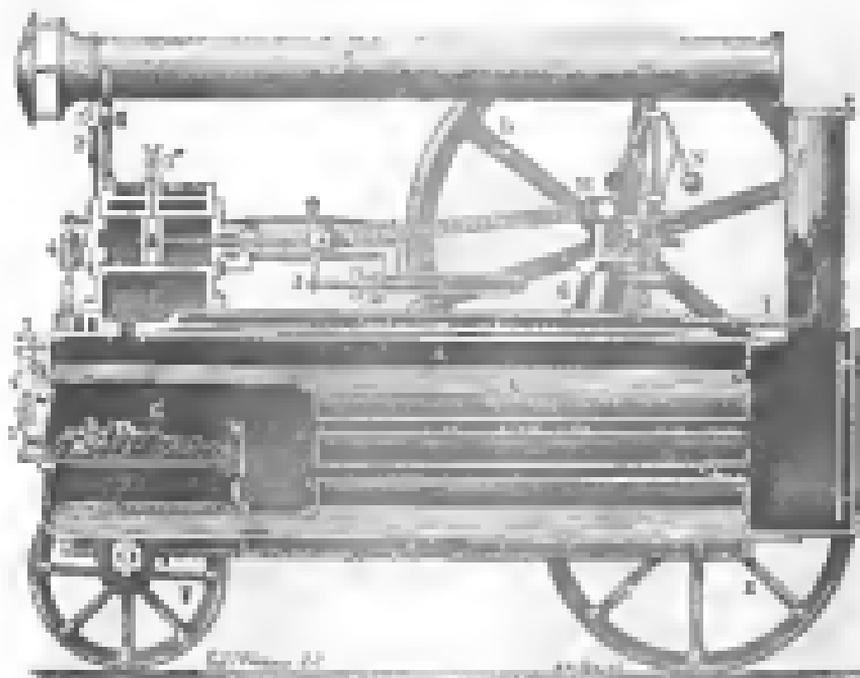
Coupe longitudinale de la machine à vapeur portable de M. Goussier, à Orléans.
